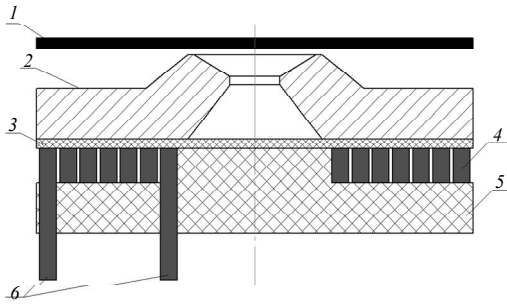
Конструктивная схема совмещенного дискового СУ: 1 – тонкостенный ферромагнитный лист металла; 2 – вторичная обмотка – индуктор-инструмент с внутренним отверстием в форме усеченного конуса; 3 – диэлектрическая прокладка; 4 – витки плоской спирали первичной обмотки СУ; 5 – диэлектрическая основа; 6 – электрические выводы первичной обмотки СУ
